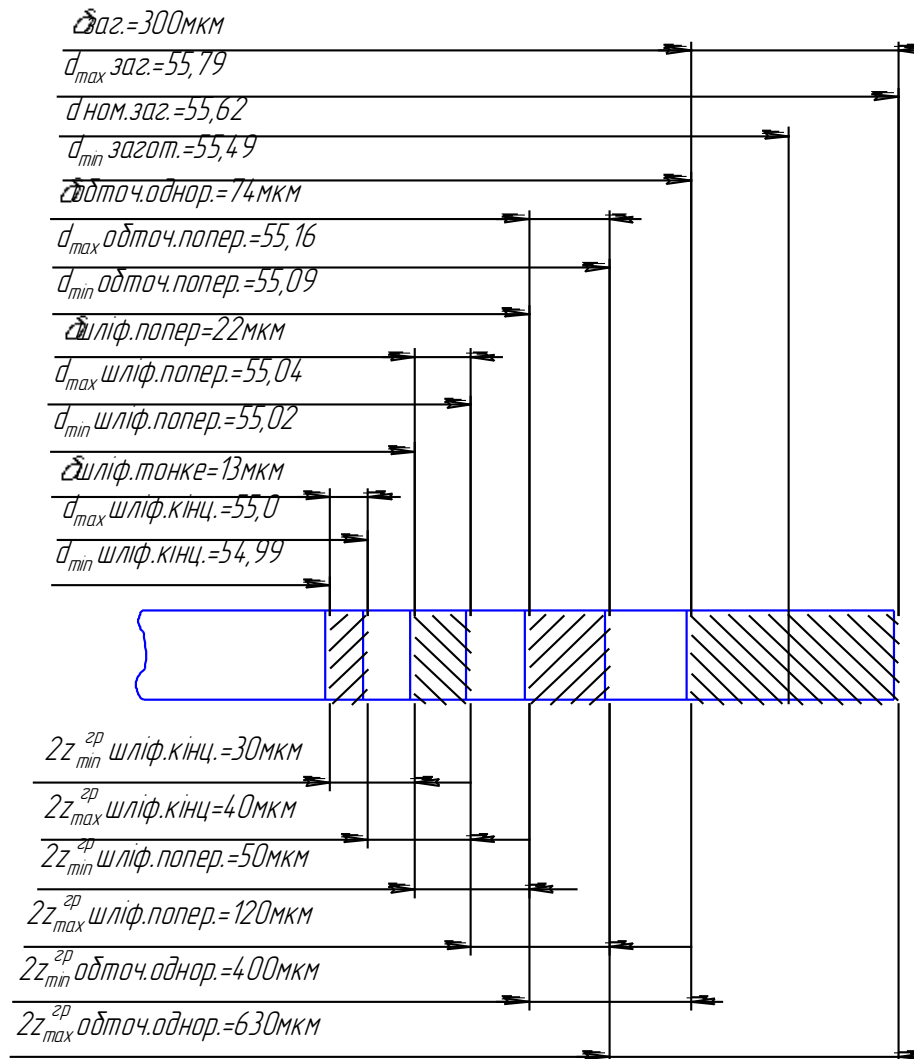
Схема розташування припусків та допусків на оброблення поверхні  $\varnothing 55$
